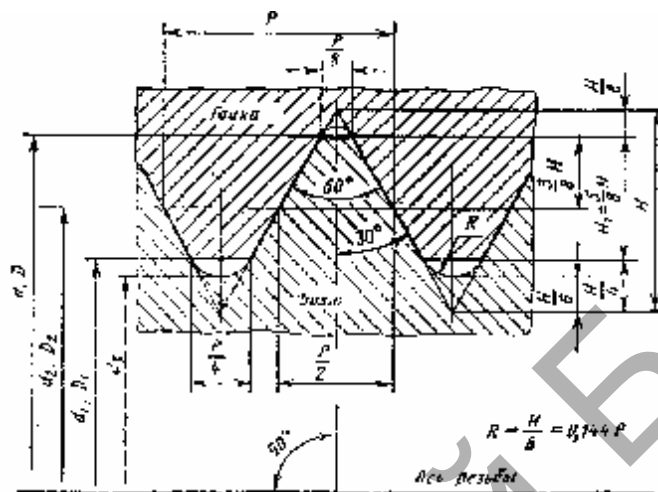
Номинальный теоретический профиль метрической резьбы
